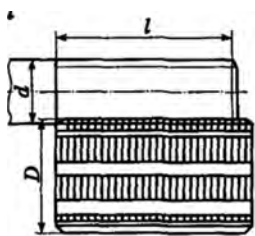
Схемы фрезерования резьбы гребенчатой фрезой
